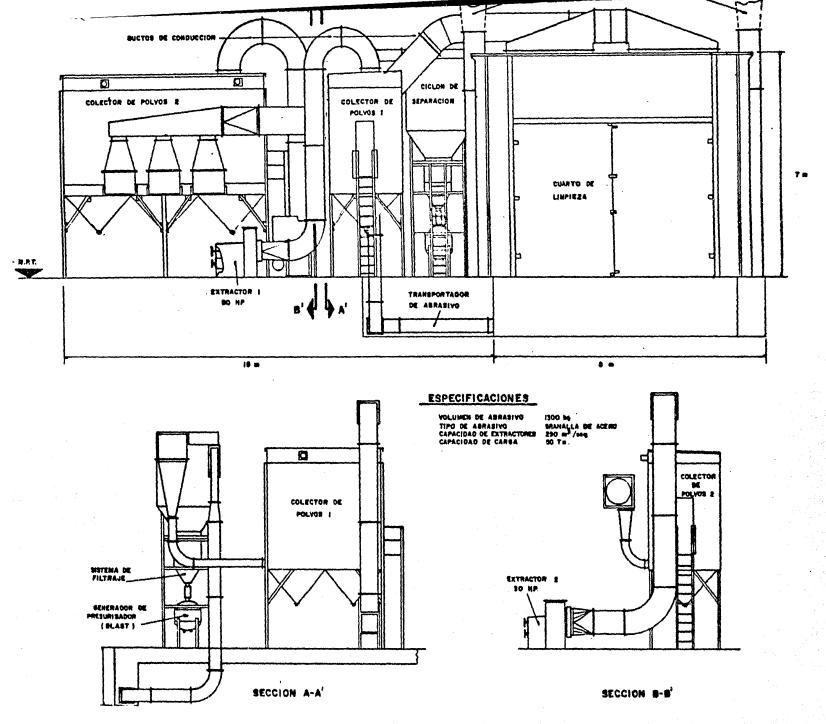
EQUIPO DE LIMPIEZA (SAND BLAST)
